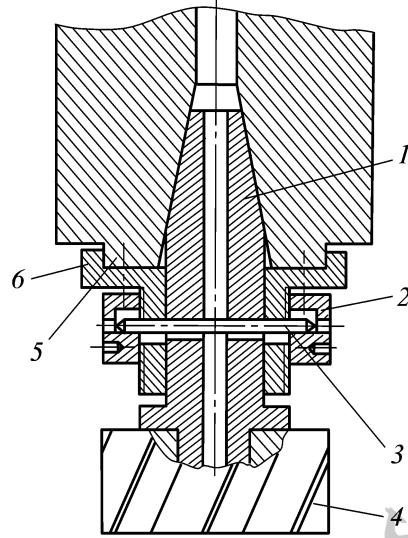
Схема устройства для механизированного крепления фрез
